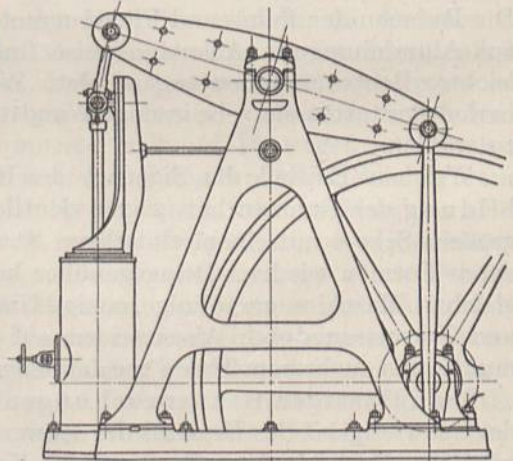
A-Rahmen einer Schwinghebelmaschine.
